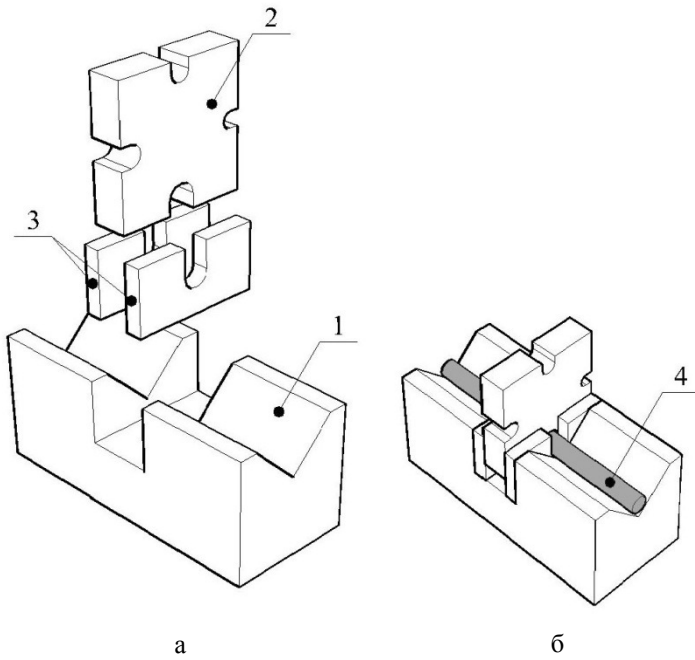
Общий вид установки для проведения испытаний поэлементно (а) и в сборе (б): 1 – держатель образцов; 2 – верхний нож; 3 – нижние ножи; 4 – испытуемый стержень композитной арматуры.
